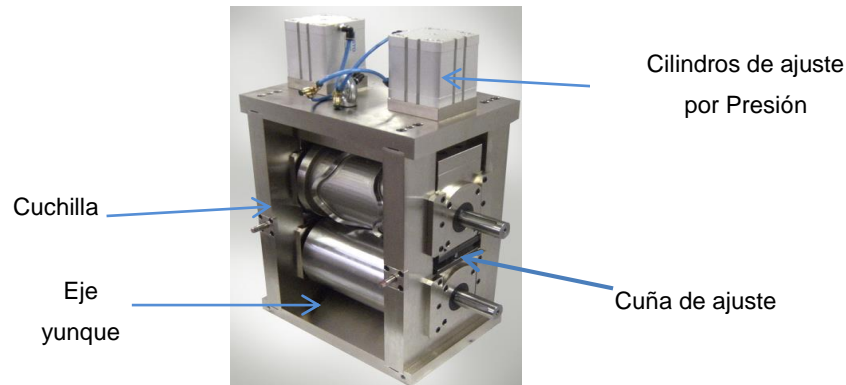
Troquel de corte tipo rotativo ajustado por presión. [5]
